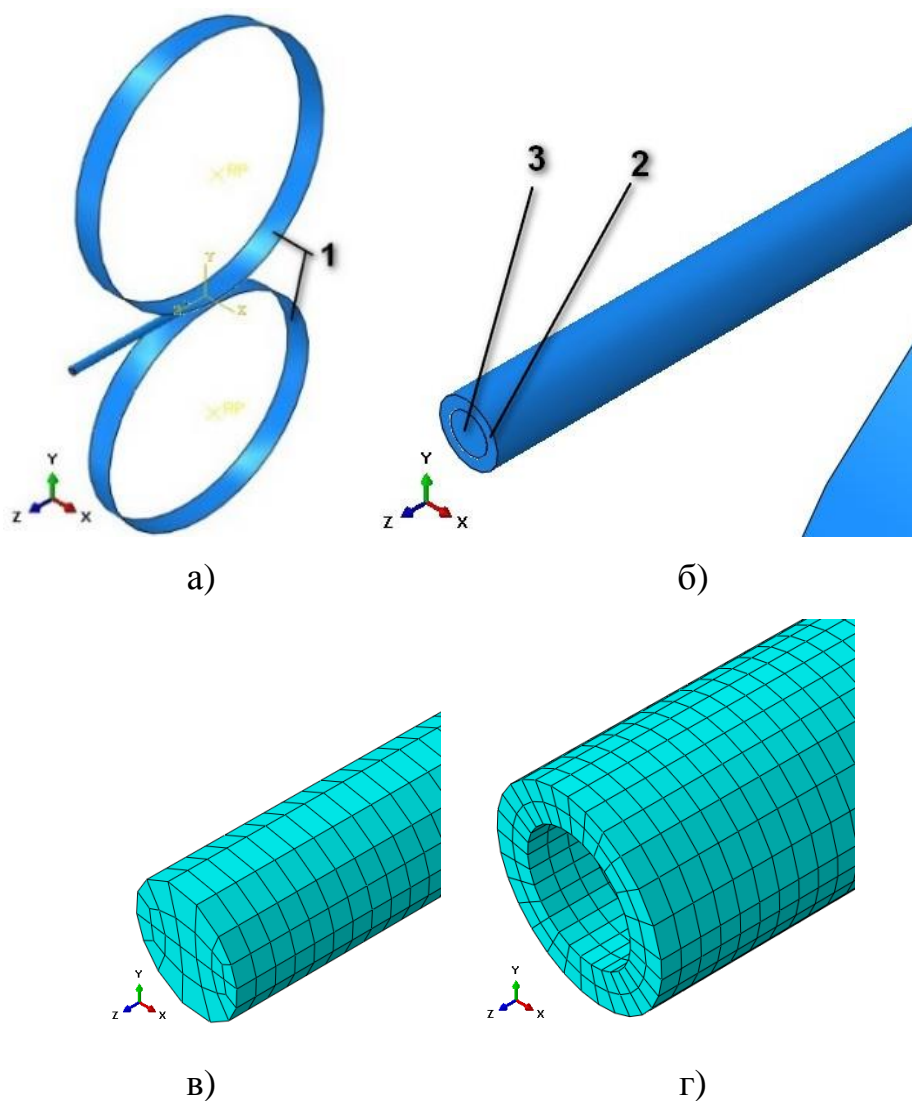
Конечно-элементная модель процесса плющения порошковой проволоки (1 – рабочие валки; 2 – металлическая оболочка; 3 – порошковый сердечник):
